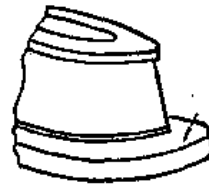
圆锥滚子轴承内圈推力挡边表面磨损
